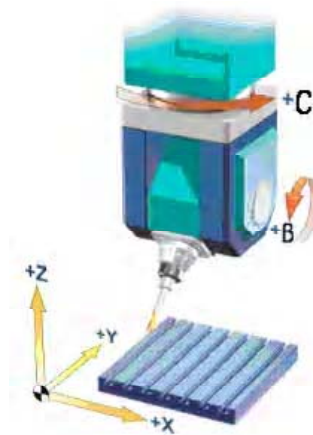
Электрошпиндель поворотной головки станка КХ-200
